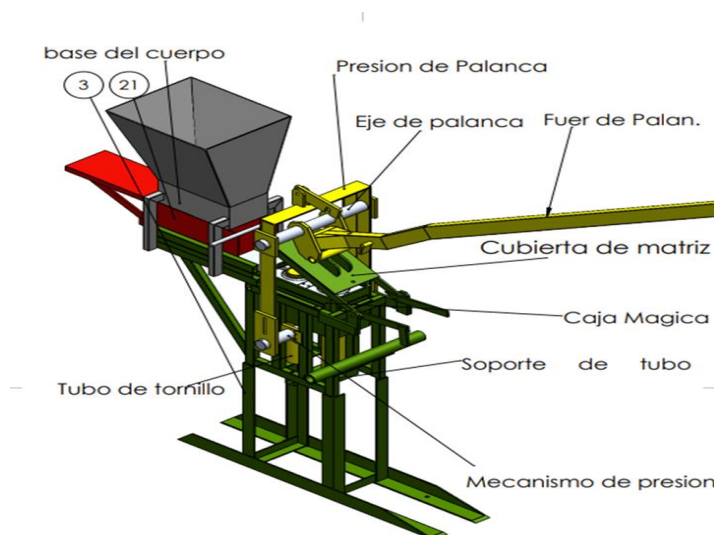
Palanca de Fuerza para el Ensamblaje de la Máquina
